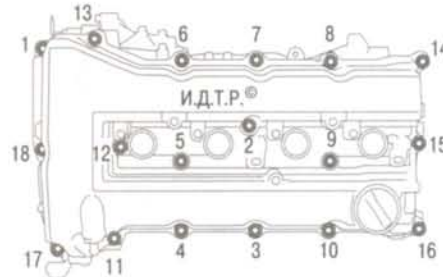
Порядок затяжки болтов крепления крышки головки блока цилиндров
